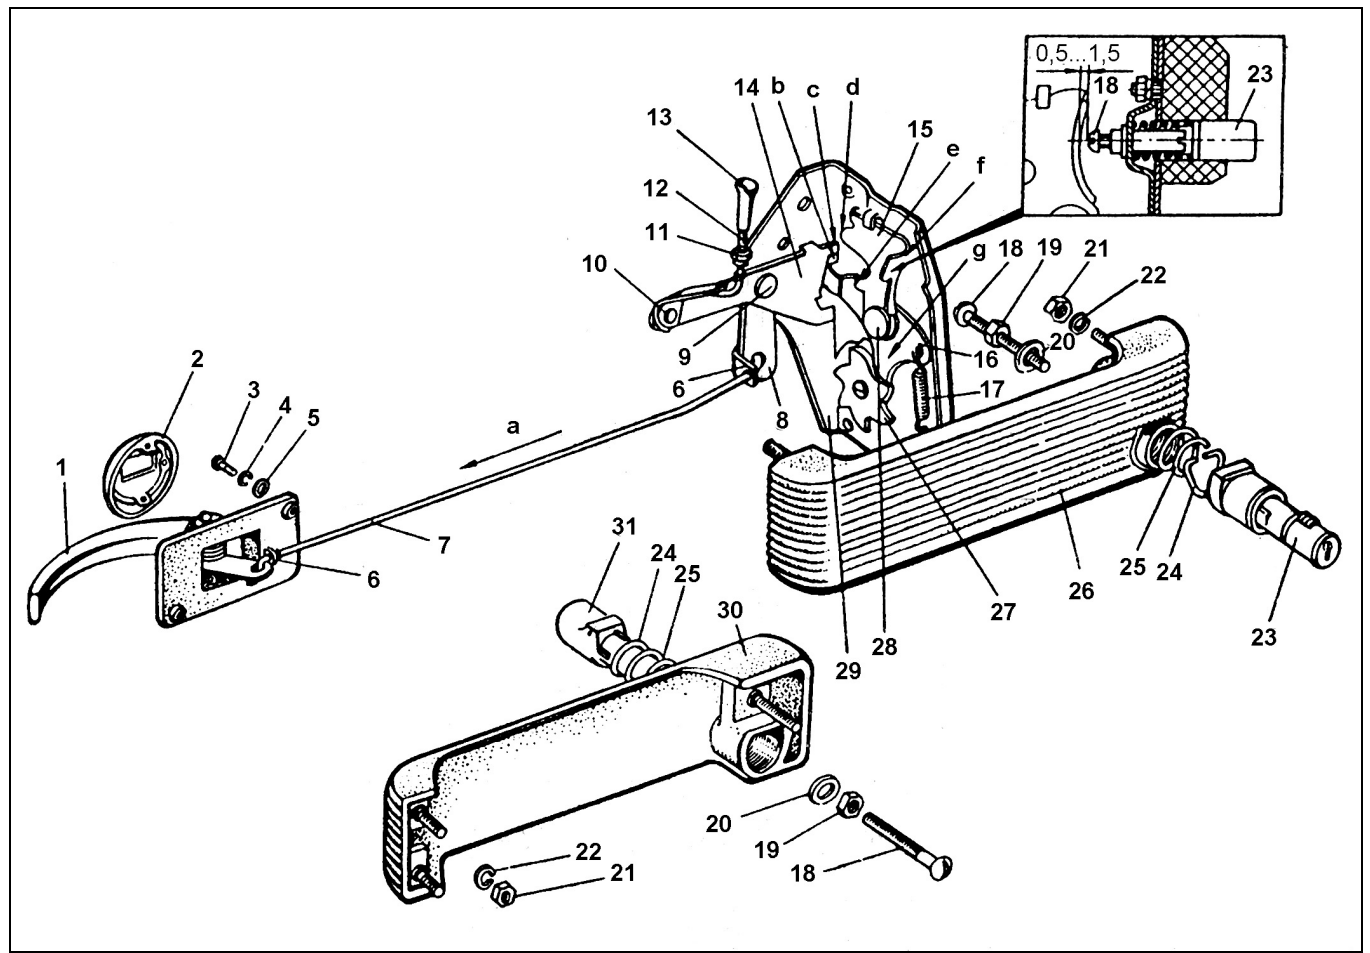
Замок, привод замка и ручки: 1 — ручка внутренняя; 2 — облицовка; 3, 18 — винт; 4, 22 — шайба пружинная; 5, 20 — шайба; 6 — прокладка; 7 — тяга; 8 — рычаг замка; 9, 28 — ось; 10 — заклепка; 11 — розетка кнопки; 12 — тяга кнопки запирающего механизма; 13 — кнопка запирающего механизма; 14 — рычаг запирающего механизма; 15 — щеколда; 16 — собачка храповика; 17 — пружина; 19 — контргайка; 21 — гайка; 23 — кнопка замочной ручки двери; 24 — скоба; 25 — пружина кнопки; 26 — ручка наружная левая; 27 — храповик; 29 — корпус замка (левый); 30 — ручка наружная правая; 31 — кнопка ручки правой двери.
